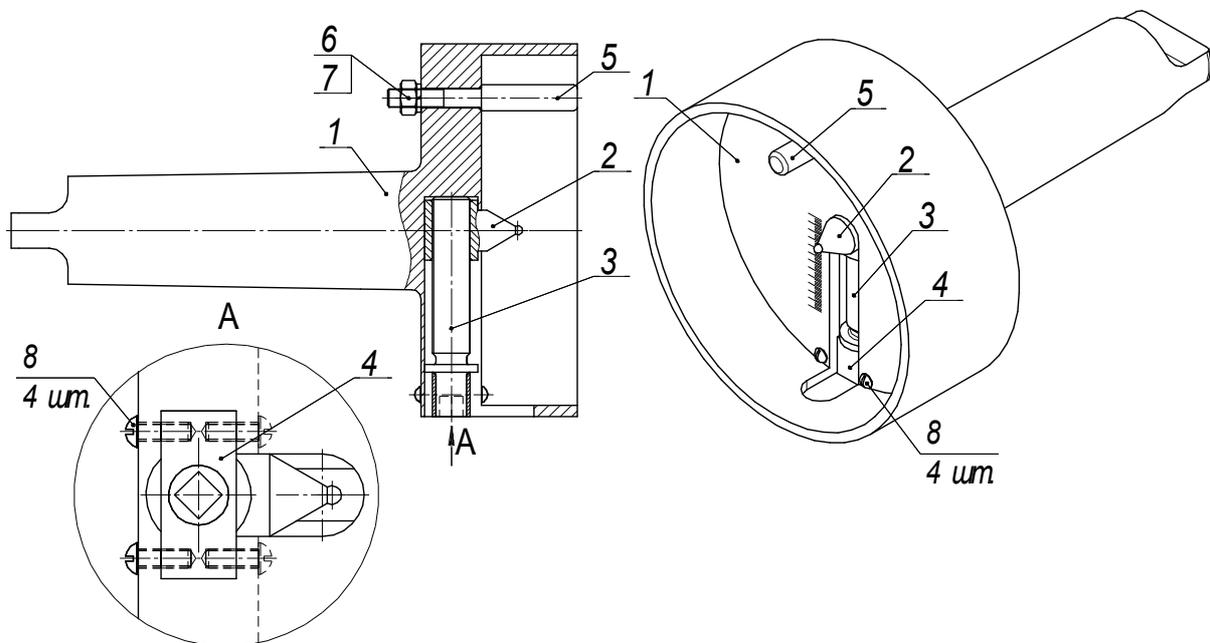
Смещаемый токарный центр: 1 – корпус; 2 – центрирующий элемент; 3 – регулировочный винт; 4 – втулка; 5 – поводок; 6 – гайка; 7 – пружинная шайба; 8 – винт
